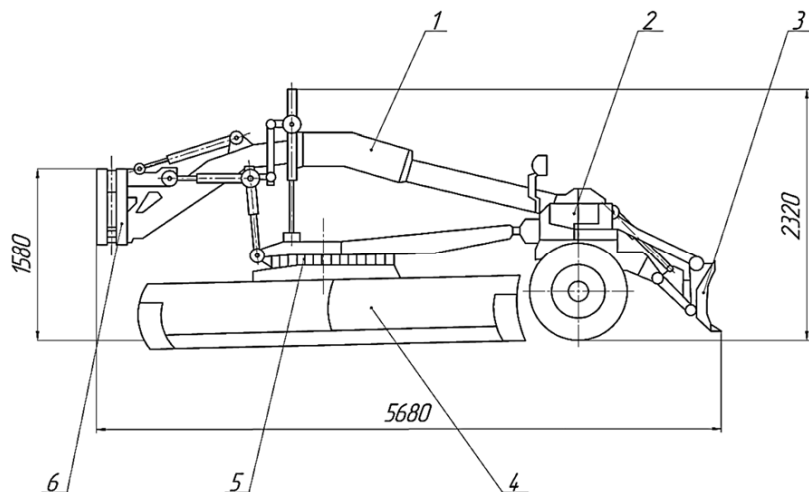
Общий вид полуприцепного грейдера с передней навеской: 1 – рама; 2 – поворотный узел; 3 – бульдозерный отвал; 4 – грейдерный отвал; 5 – поворотный круг; 6 – шарнир поворота рамы
